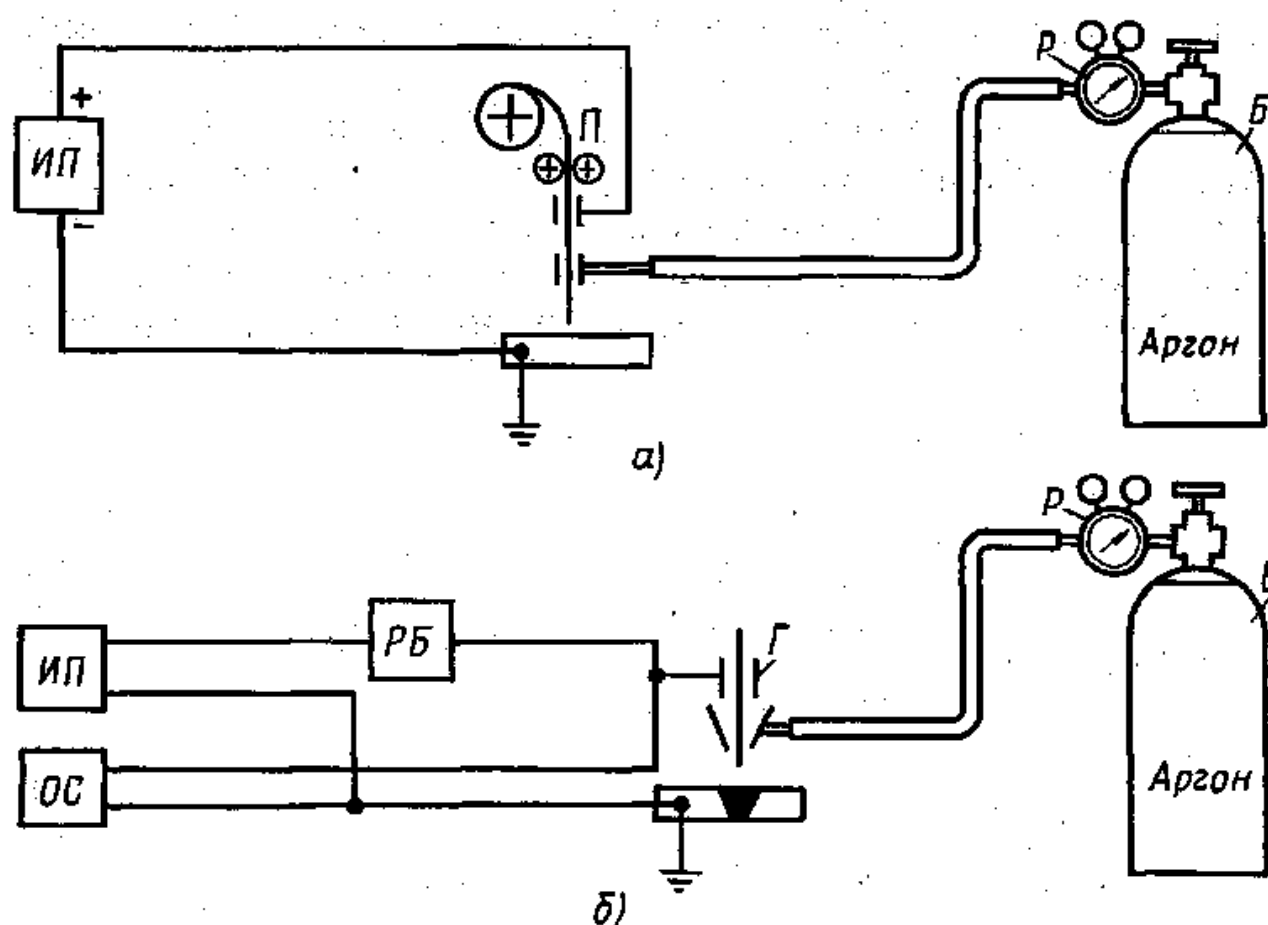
Схема поста для аргоновой сварки: а — полуавтоматической, б — ручной; ИП — источник питания, П — полуавтомат, ОС — осциллятор, РБ — реостат, Г — горелка, Р — редуктор, Б — баллон
